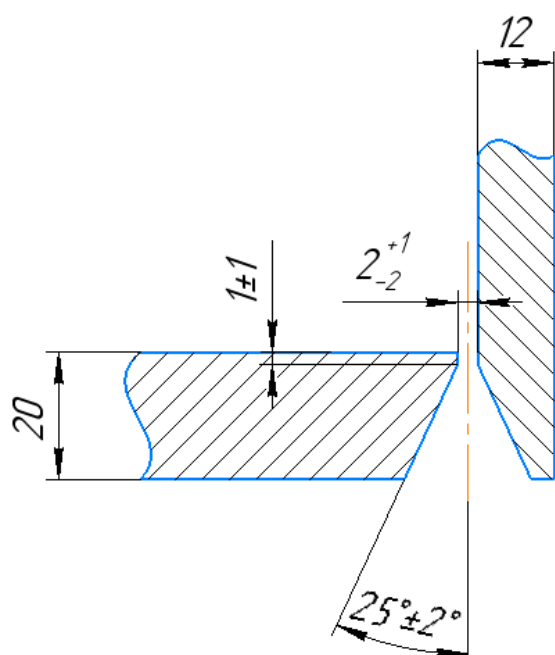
Подготовка кромок свариваемых деталей тип сварного соединения У10 по ГОСТ 5264-80
